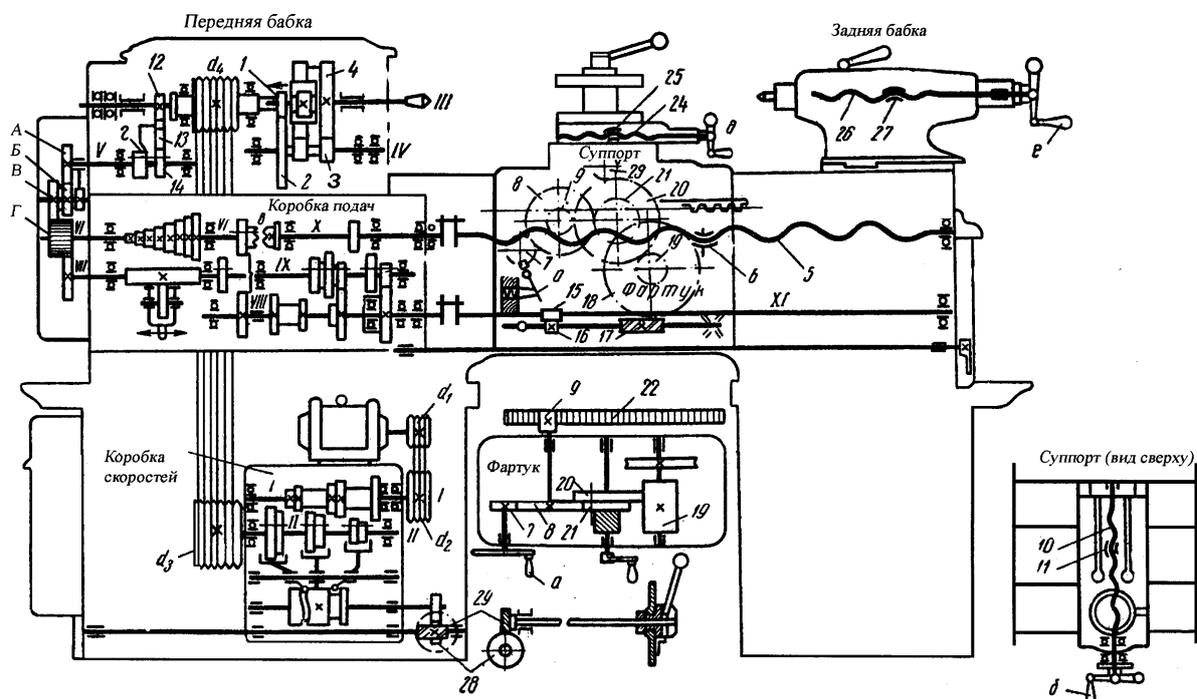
Кинематическая схема токарно-винторезного станка модели 1Е61МТ
